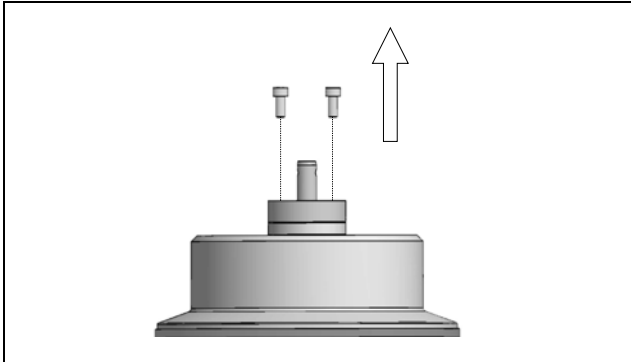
Desserrage et retrait des vis à tête cylindrique
